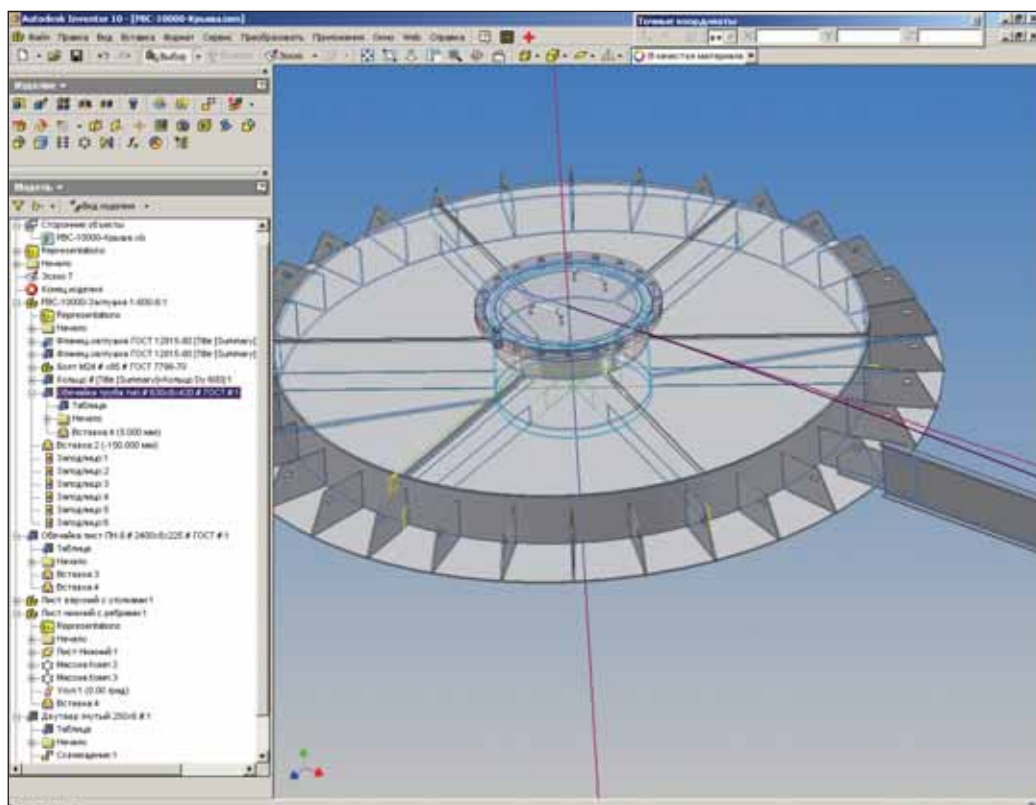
Модель сборки укрупненных щитов сферической крыши резервуара
